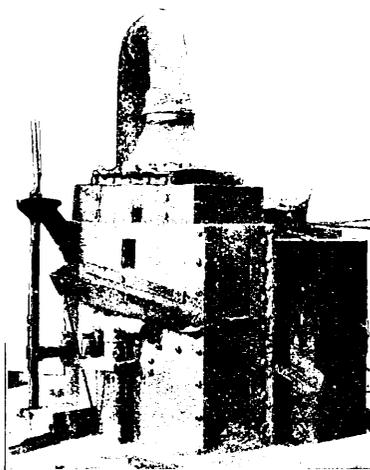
Heizrohr-Schweißfeuer und Schweißmaschine, von hinten.
